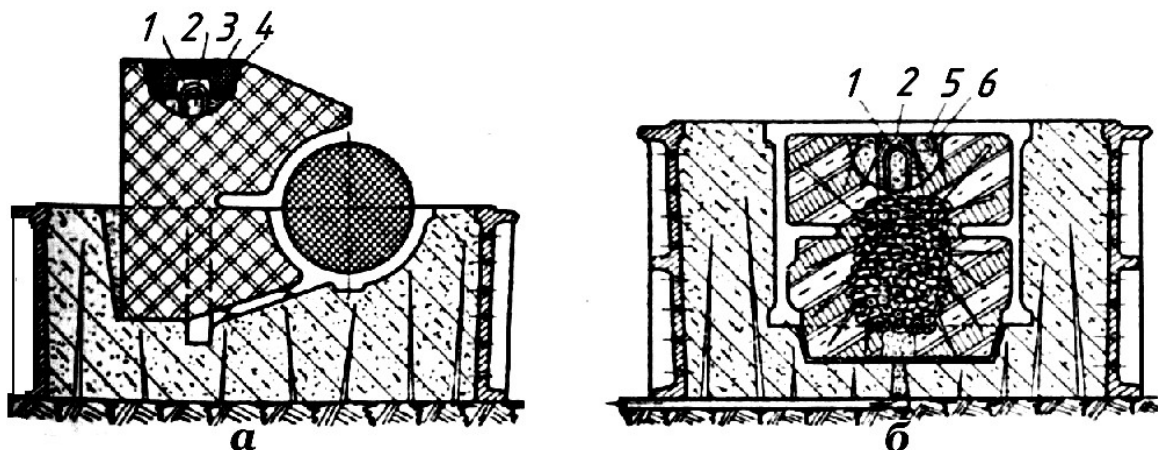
Способы заделки весок: а – при помощи стержня, б – формовочной смесью
